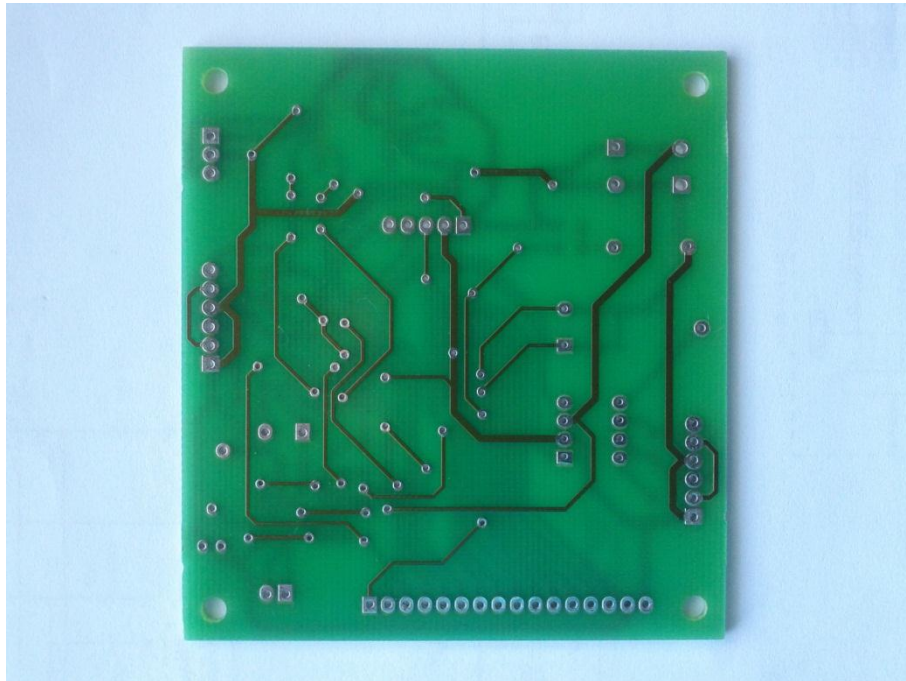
Mikrokontrolör kartı PCB çizimi
